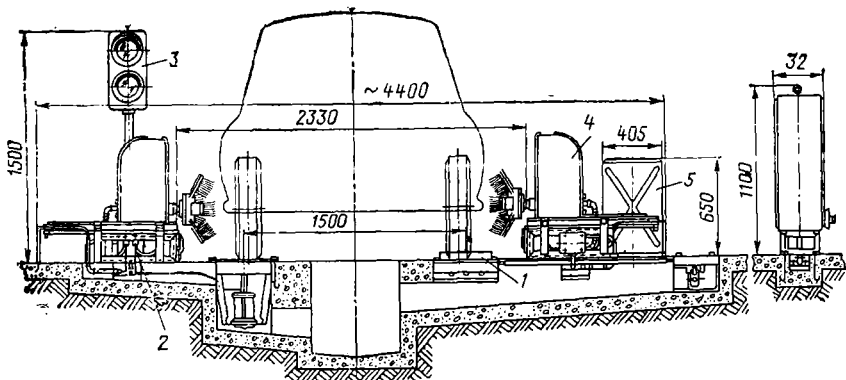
Установка для мойки колес легковых автомобилей (модель ЦКБ 1144); 1 — педали автоматического включения; 2 — пневматический захват колеса; 3 — светфор; 4 — моющий механизм; 5 — регулятор режима установки
